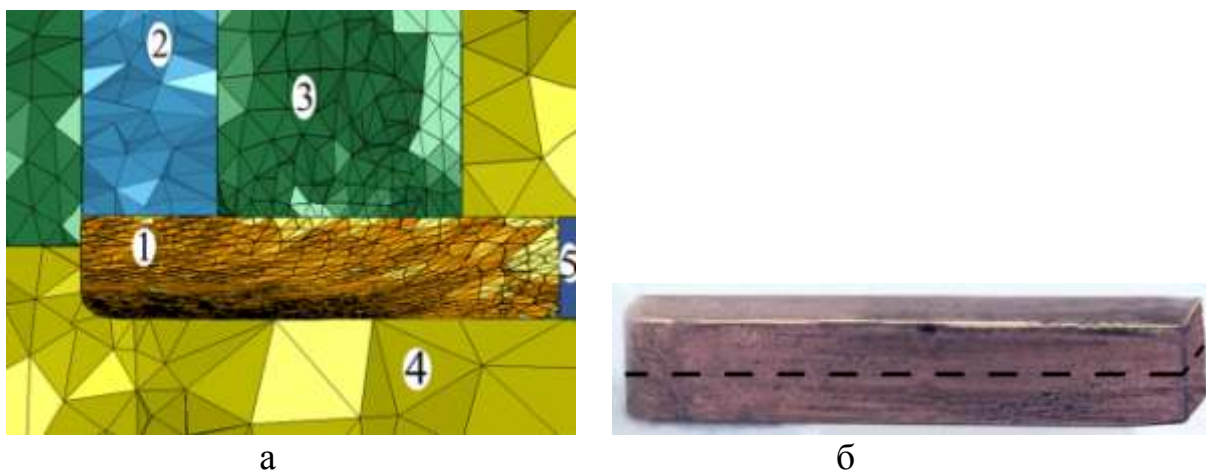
Схема процесса РКУП – а и фото образца – б: 1 – заготовка; 2 – пуансон; 3 – полуматрица верхняя; 4 – полуматрица нижняя; 5 – контрпуансон
